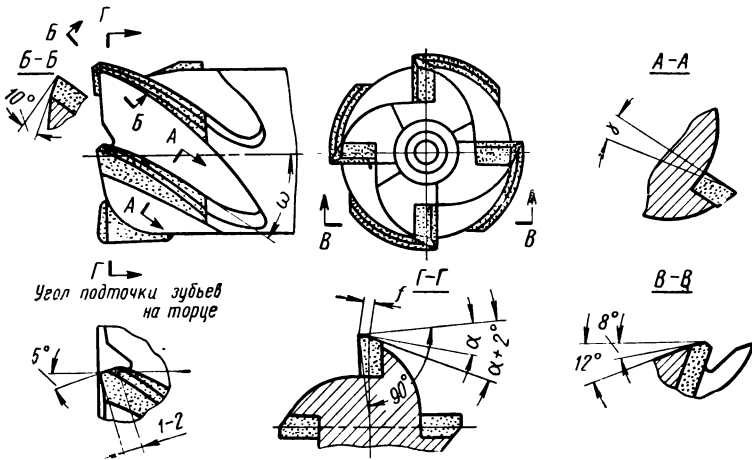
Геометрические параметры режущей части концевых фрез с винтовыми пластинками из твердого сплава
